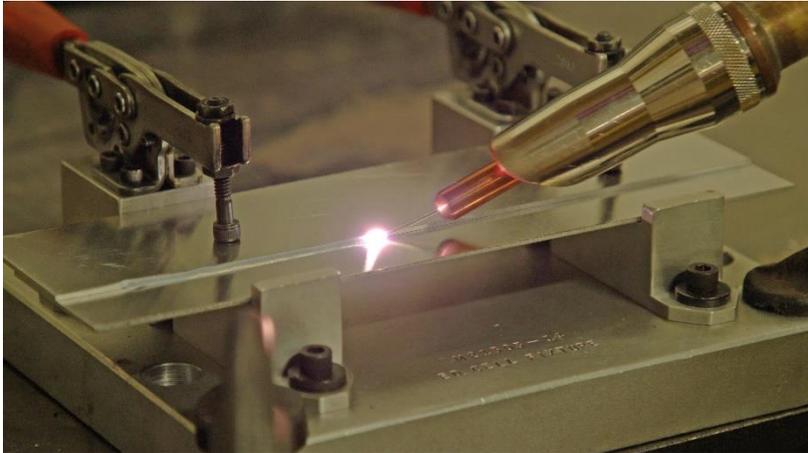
Aluminiumschweißen mit Heißdraht. ©Lincoln Electric
